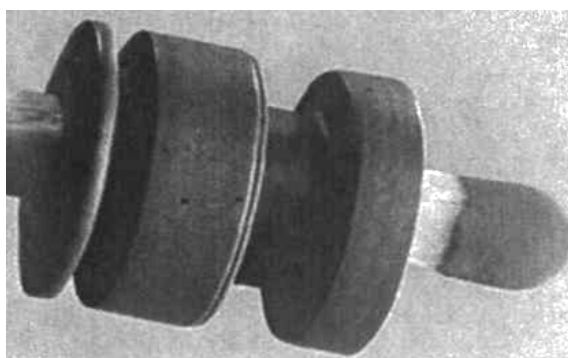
Приклад вирізу, вилито на корпусі насадки з цементованого карбіду
